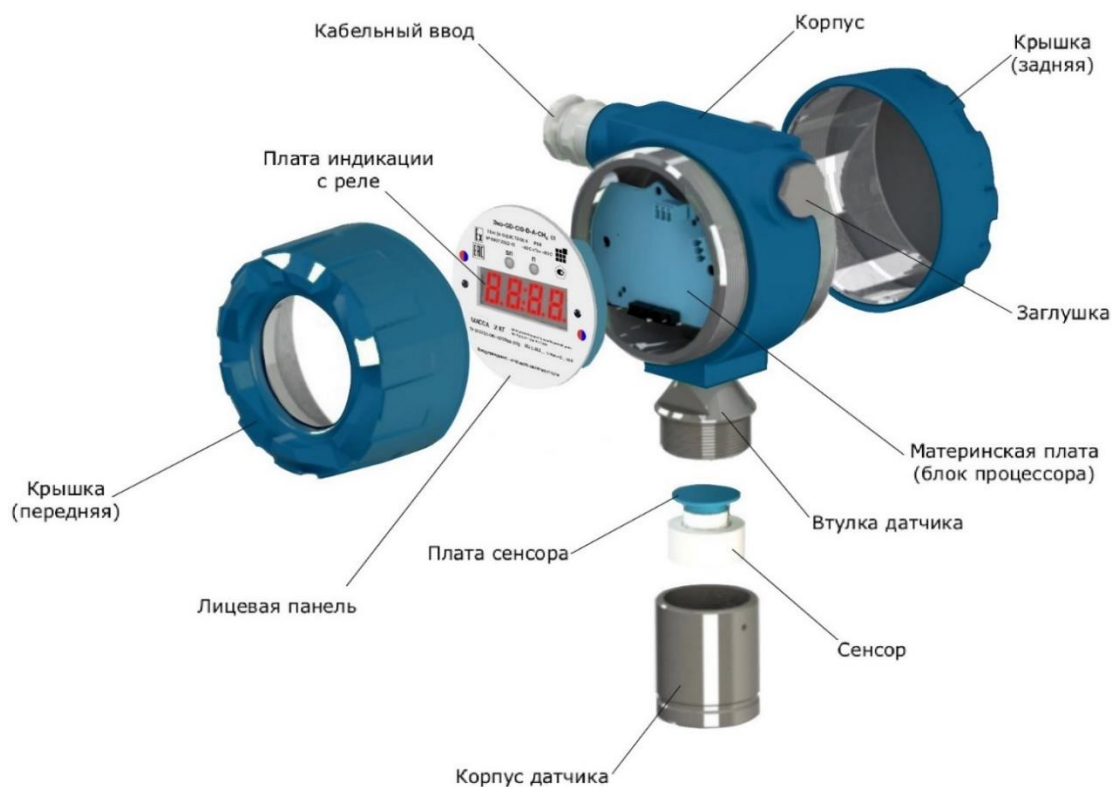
Газоанализатор в корпусе типа "D" (вид спереди)
